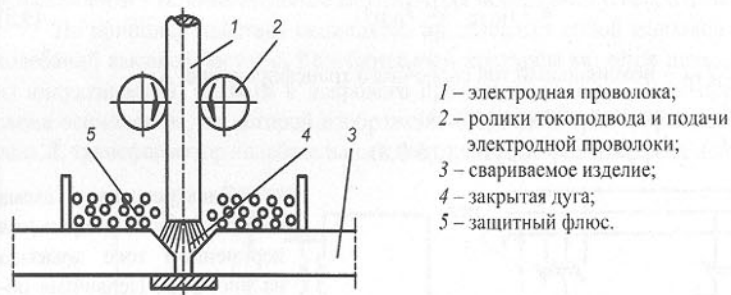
Принцип автоматической сварки под слоем флюса
